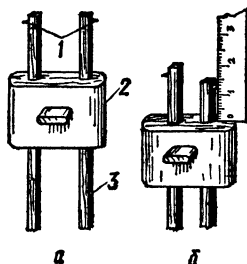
Рейсмус (а) и установка нужного размера (б):
